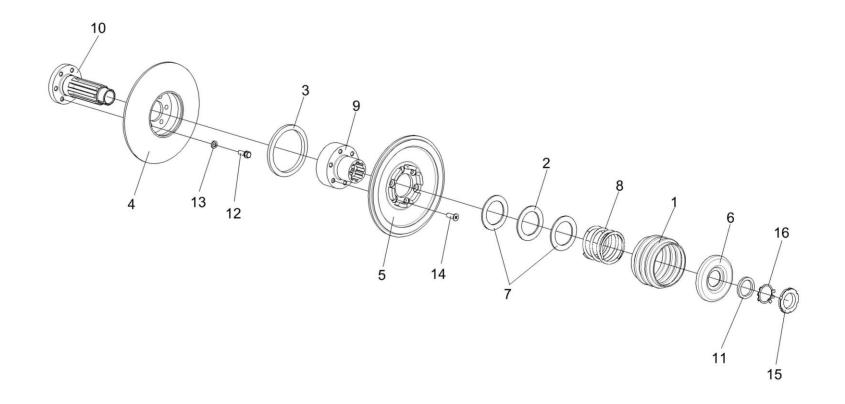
Очистка, шкив ведомый КЗК-12-0217400 и контрпривод вариатора КЗК-7-0202500Б
